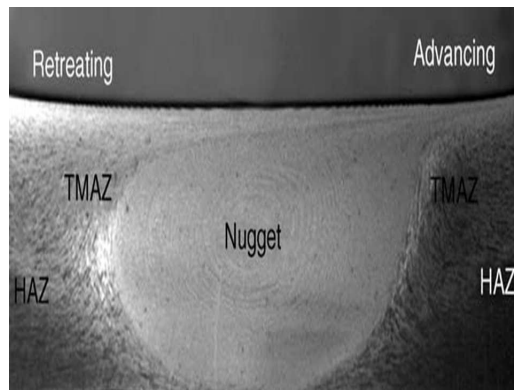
Coupe d'une soudure sur un alliage d'aluminium 7075Al-T651
